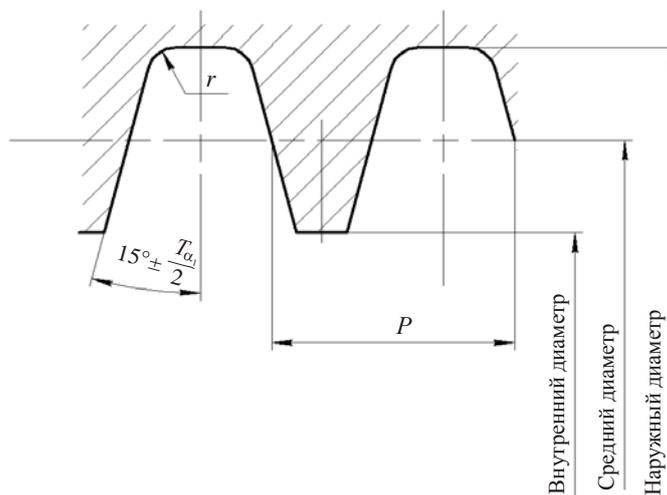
Полный профиль резьбы калибров-колец и скоб для контроля наружной трапецевидальной резьбы
